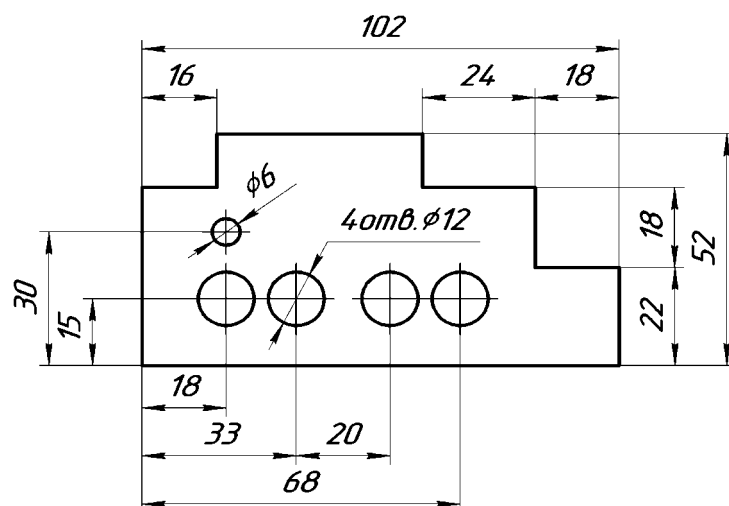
Пример нанесения размеров детали «Пластина»
